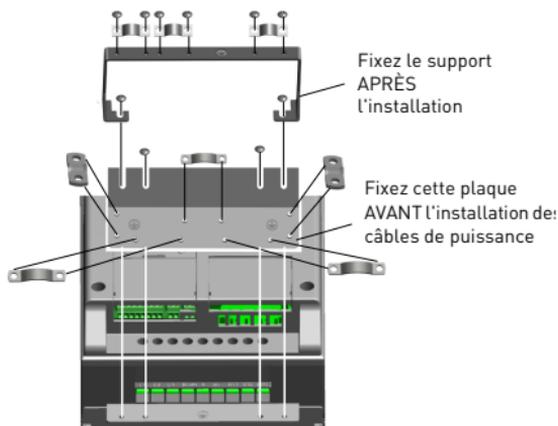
Montage de la plaque PE et du support de câble API, MI4 - MI5
